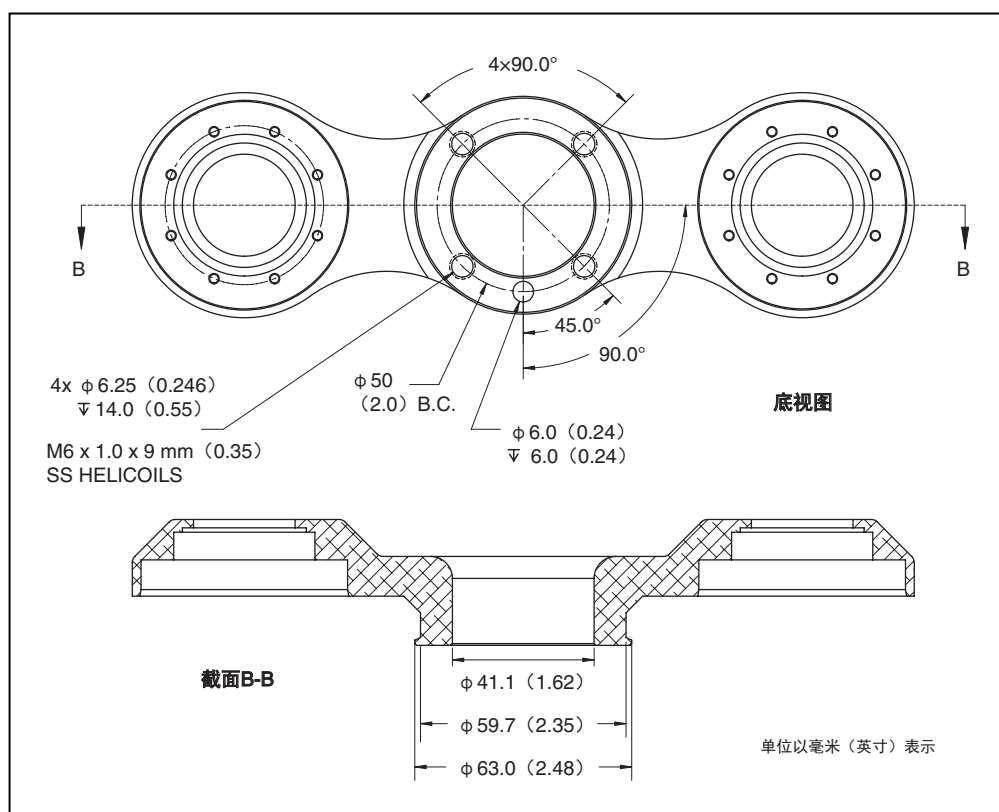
工具法兰尺寸，P31 机器人旋转平台
